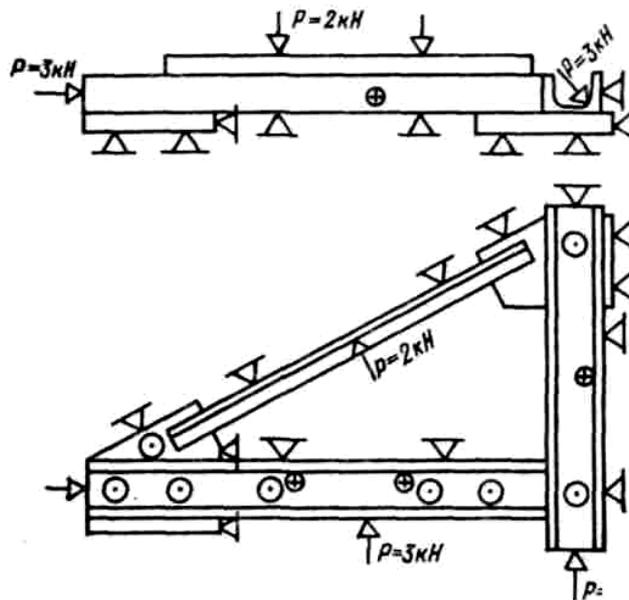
Принципиальная схема приспособления для сборки кронштейна
